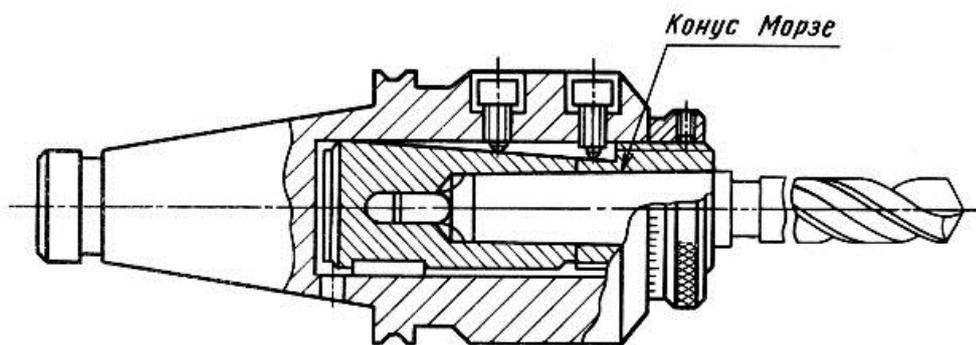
Сборная втулка с установленным сверлом с конусом Морзе
